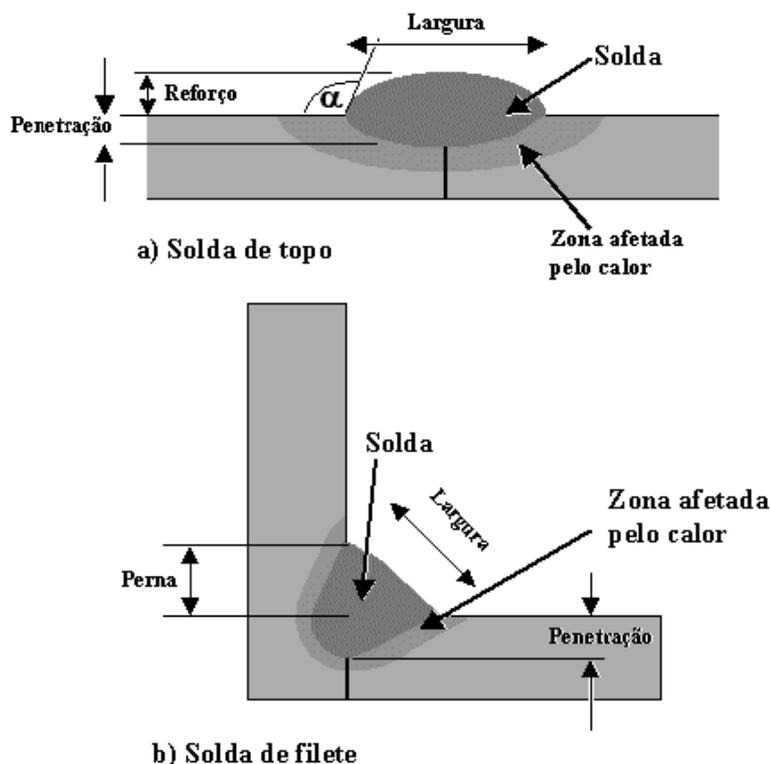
Geometria das soldas (A) de topo e (B) de filete.
